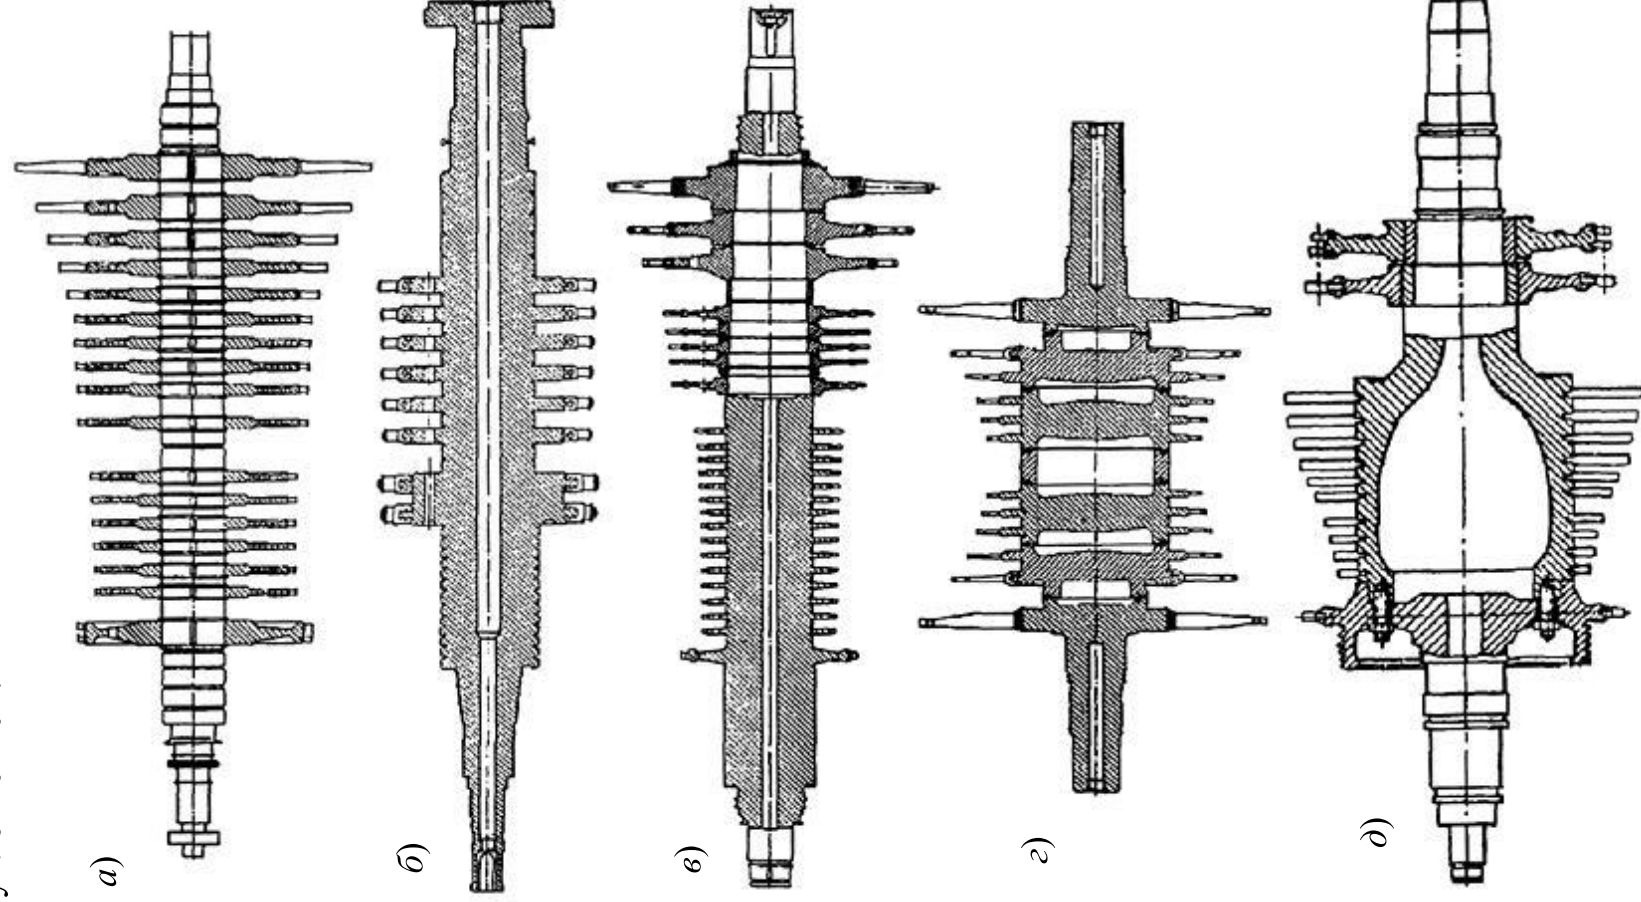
Конструкции роторов: *а* – ротор с насадными дисками; *б* – цельнокованный; *в* – комбинированный; *г* – сварной; *д* – барабанного типа
